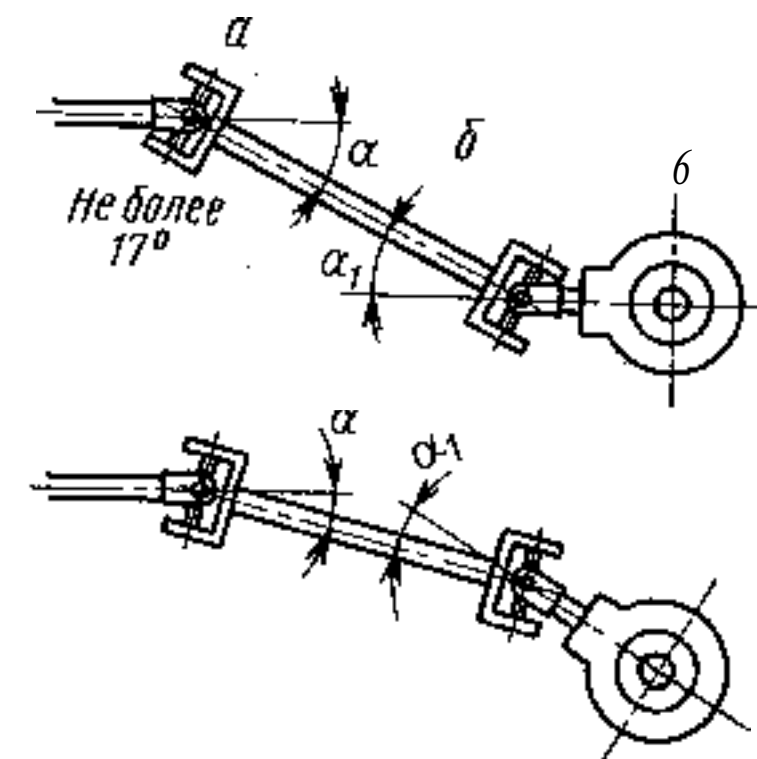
Схема соединения карданной передачи: а — карданный шарнир; б — вал кардана; в — редуктор заднего моста
